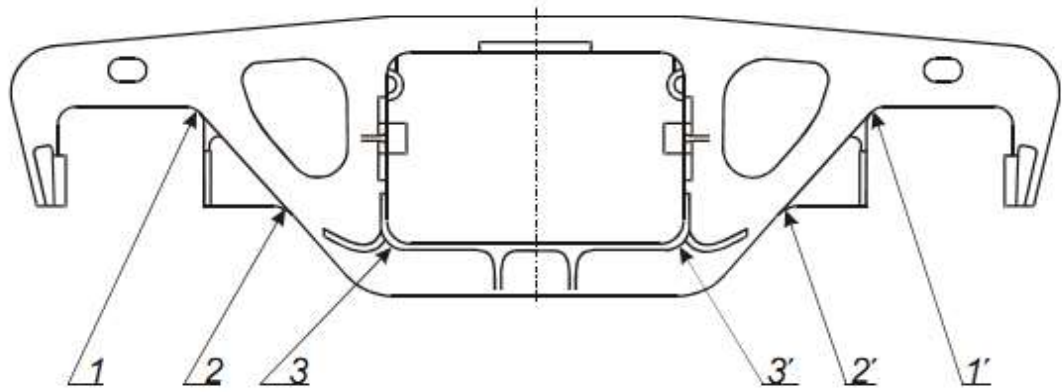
Схема расположения сечений в боковой раме по зонам разрушения: 1 – сечение внутреннего угла буксового проема; 2 – сечение наклонного пояса за опорной площадкой; 3 – сечение рессорного проема
